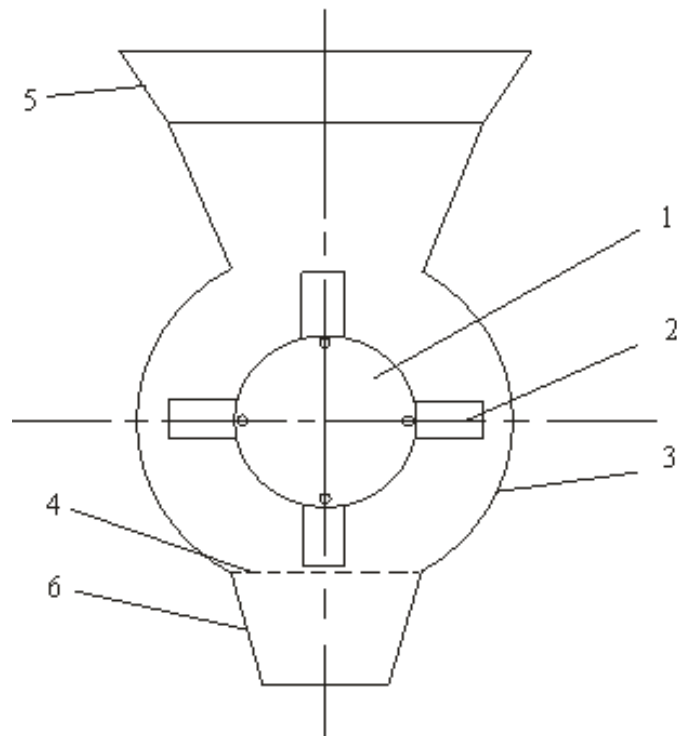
Конструктивна схема молоткової дробарки: 1 – ротор; 2 – молоток; 3 – корпус; 4 – решето; 5 – бункер; 6 – вивантажувальний рукав
